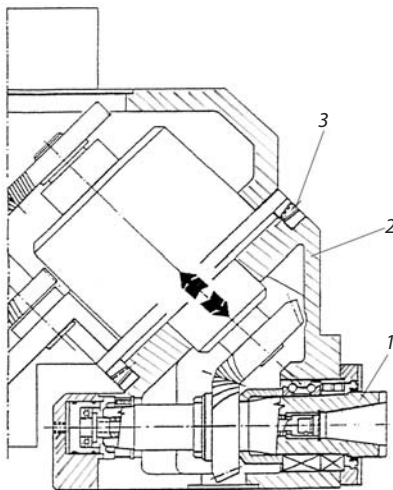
Конструктивная схема поворотной шпиндельной головки
